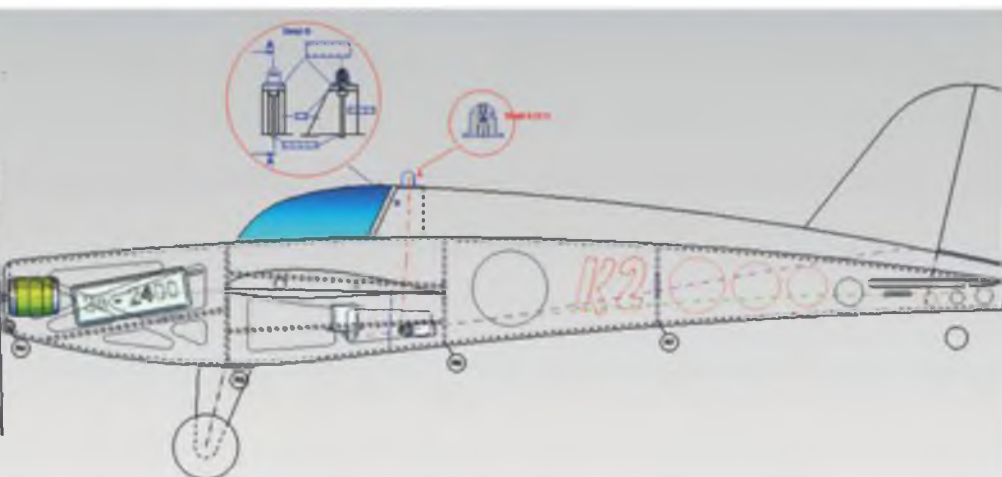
Der Bauplan des Rumpfes ist fast fertig. ▼
